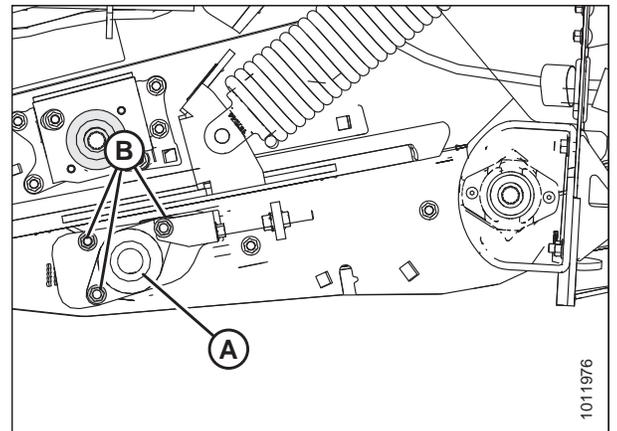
Rodillo tensor de la cama frontal del lado izquierdo
